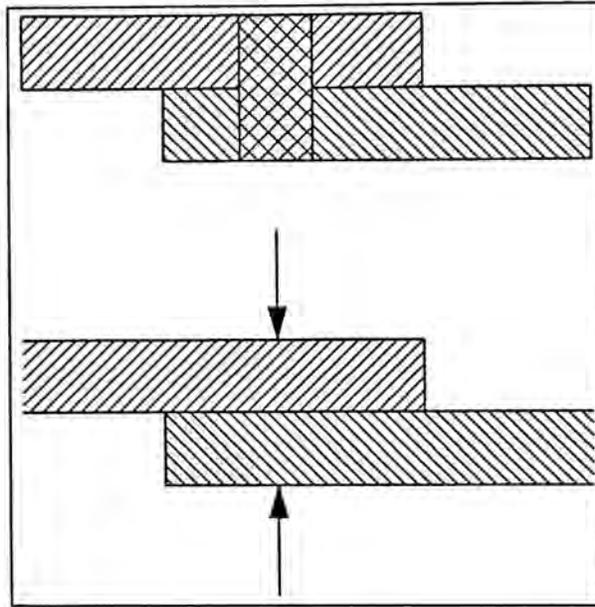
Wirkstrukturen für die Anpassung die Werkzeugplatten
